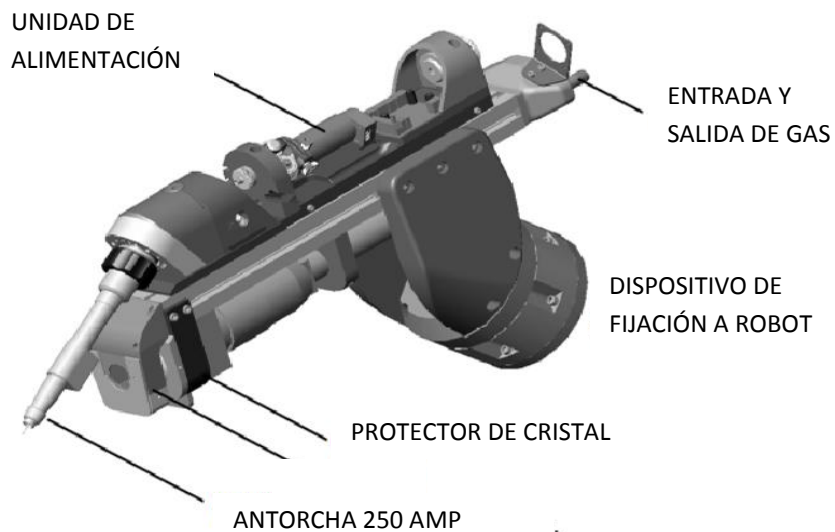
Representación esquemática de la pistola de soldar híbrida para robot soldador (3)
